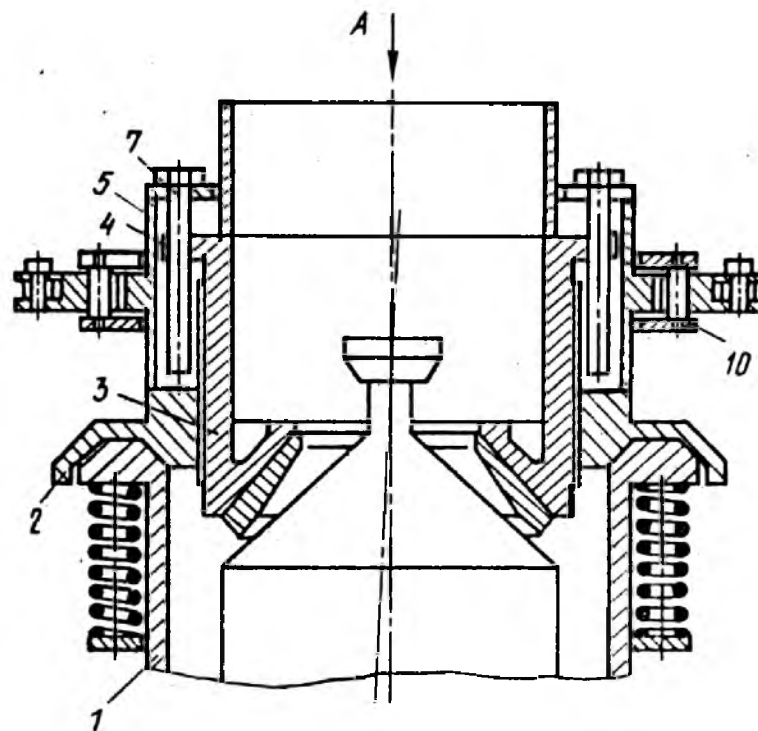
Пристрій для регулювання розвантажувальної щілини конусної дробарки, вигляд А – А
